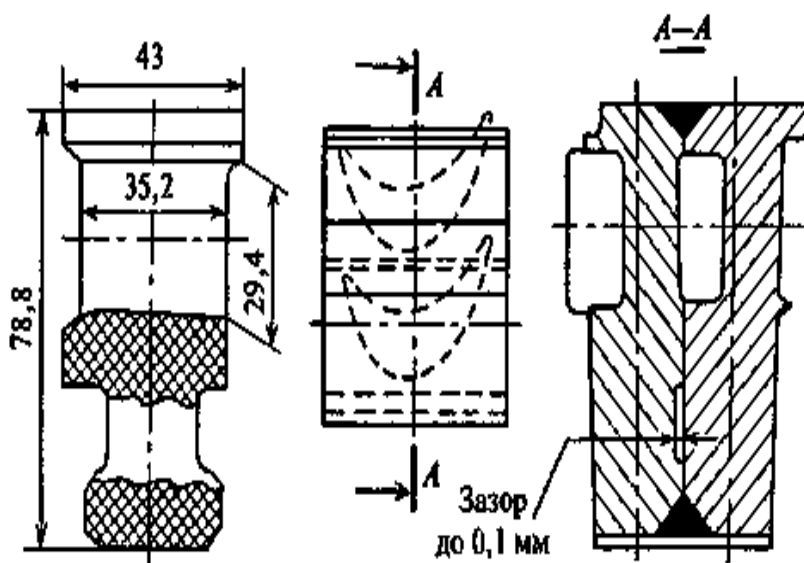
Сварной пакет из двух лопаток ЛМЗ
